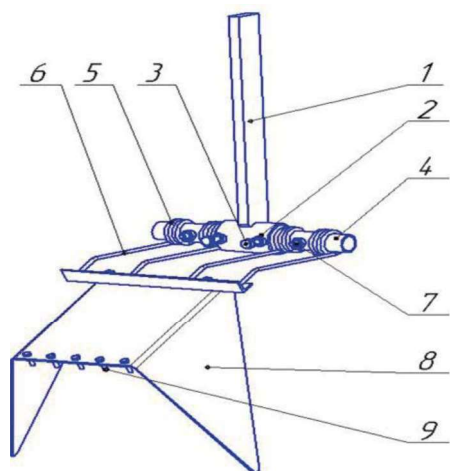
Схема устройства для формирования узкопрофильных гряд для установки на агрегат универсальный АУ-М2 (вид сбоку): 1 – стойка; 2 – втулка; 3 – болты стопорные; 4 – труба несущая; 5 – пружина кручения; 6 – зубья; 7 – болт фиксирующий; 8 – кожух устройства для формирования гряд; 9 – рыхлительные зубья
